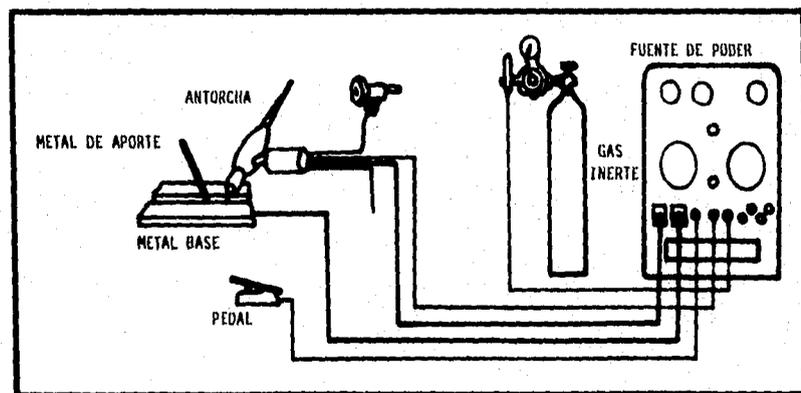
DETALLE DEL PROCESO DE SOLDADURA GTAW.
